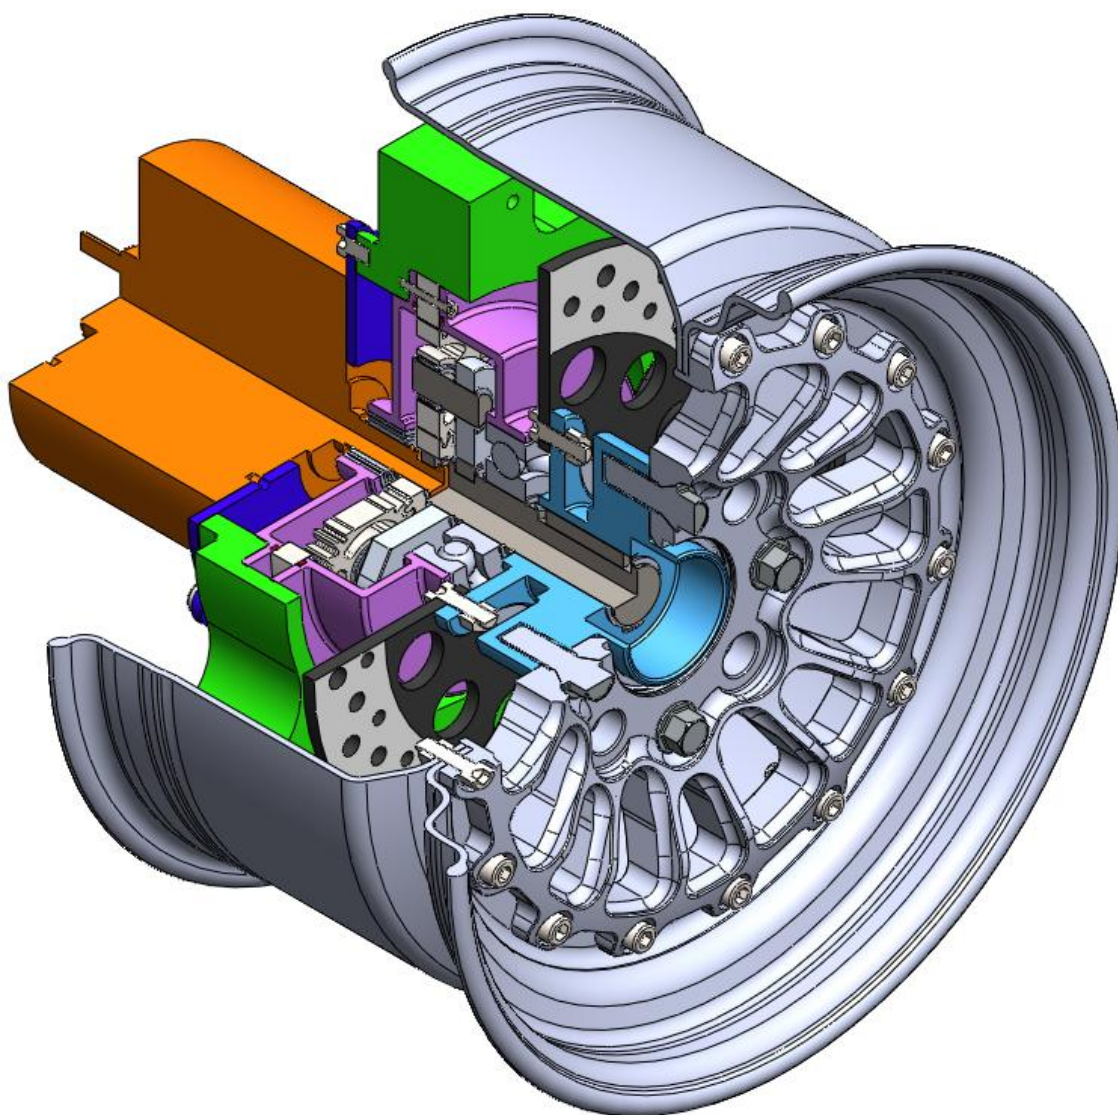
Vista de corte de sección del ensamblaje CAD 3D del sistema de transmisión IWM propuesto.
